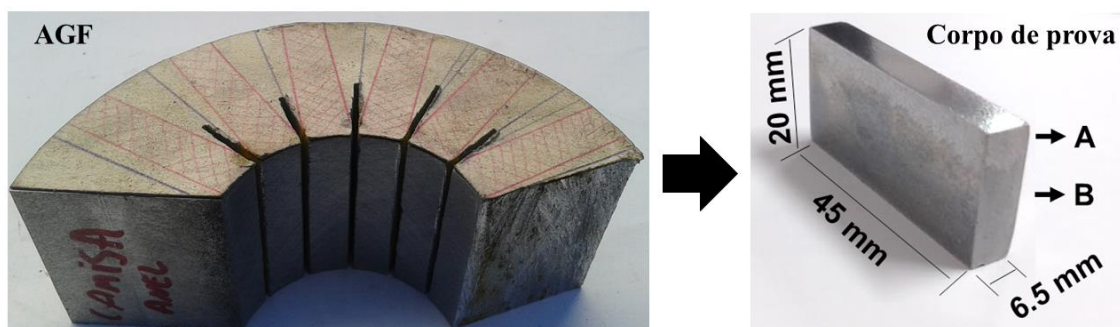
Dimensões dos corpos de prova usinados a partir do AGF.
